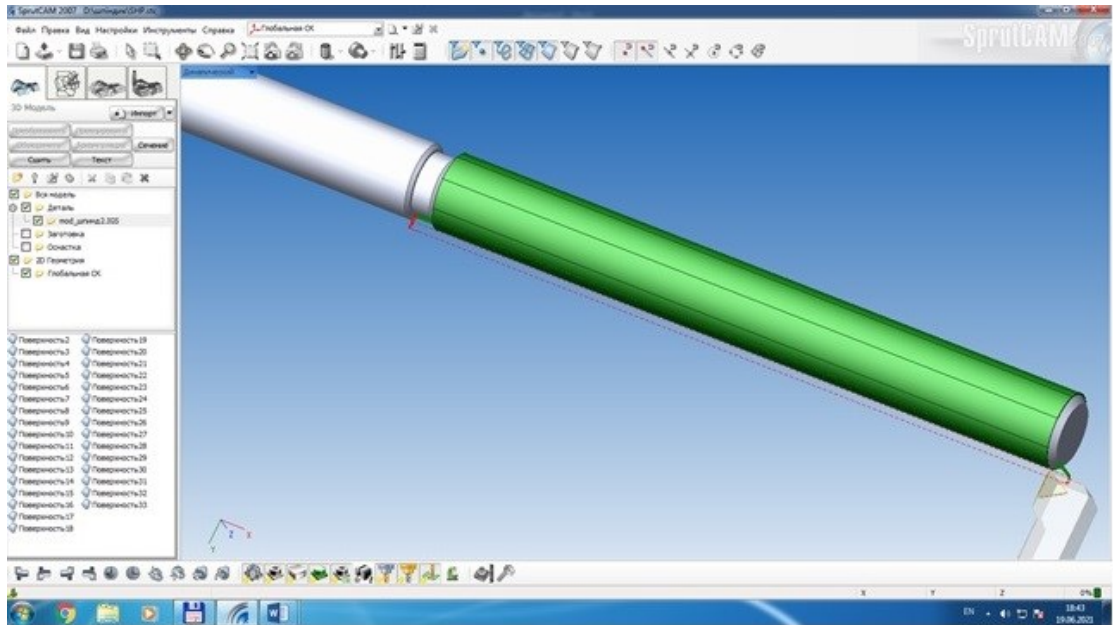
Заготовка з оброблюваною поверхнею та різьбовий різець
